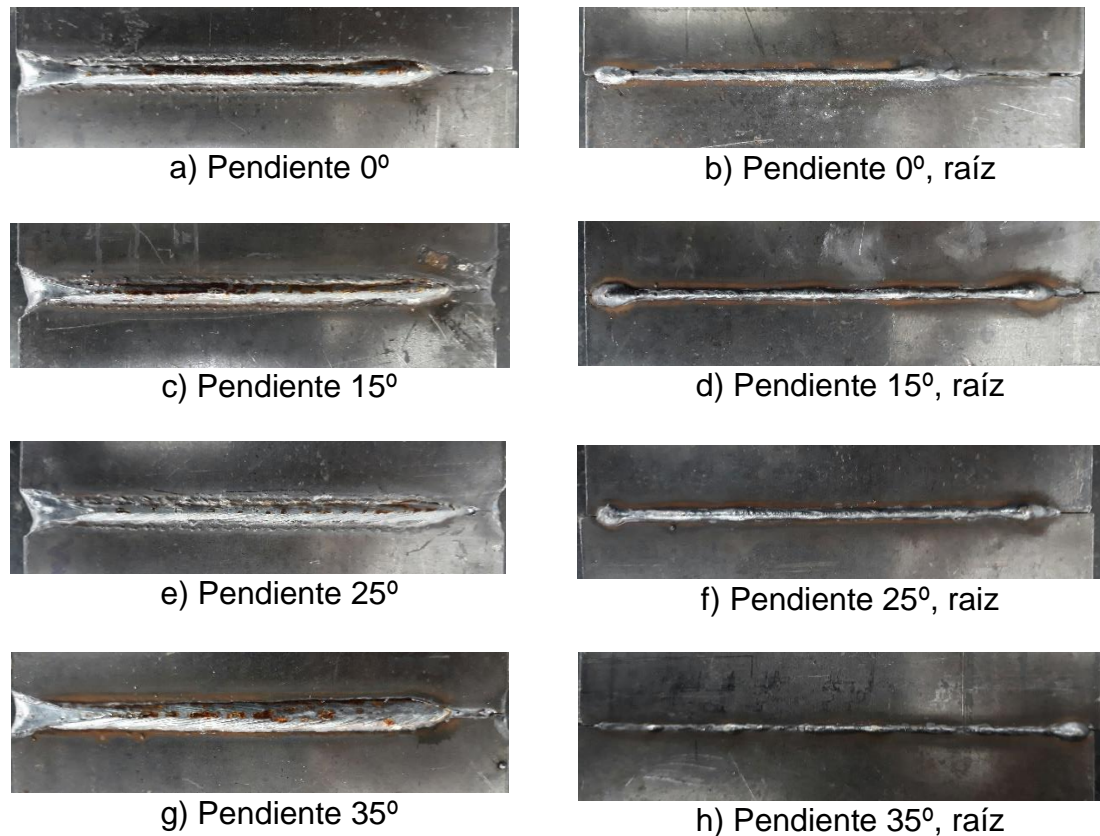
13. Aspecto superficial de la soldadura HLAW,
